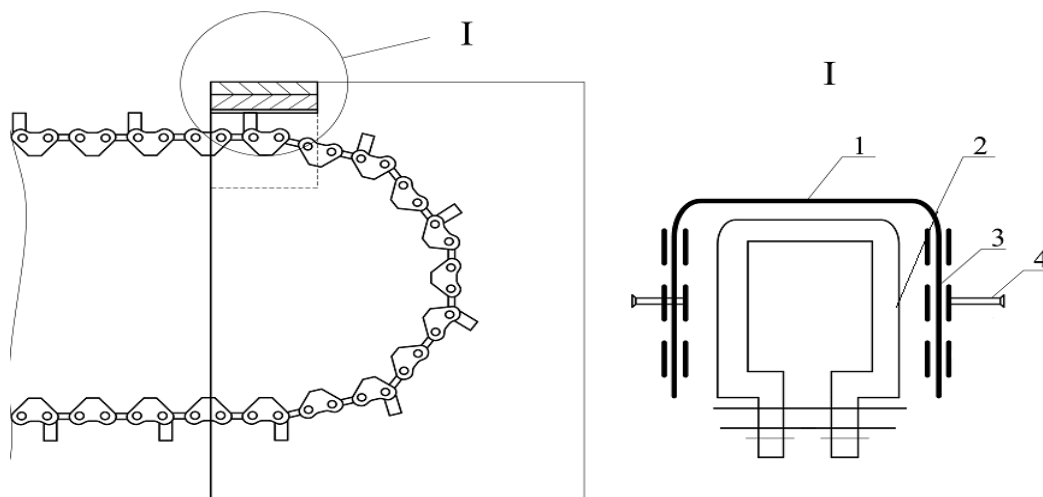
Пильная цепь новой конструкции и устройство для ее быстрой заточки: 1 – заточное устройство; 2 – зуб цепи; 3 – боковые точильные камни; 4 – передвижной блок
